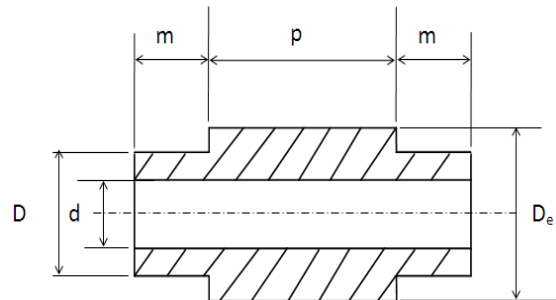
Cotas dimensionales de referencia de cojinete horizontal
